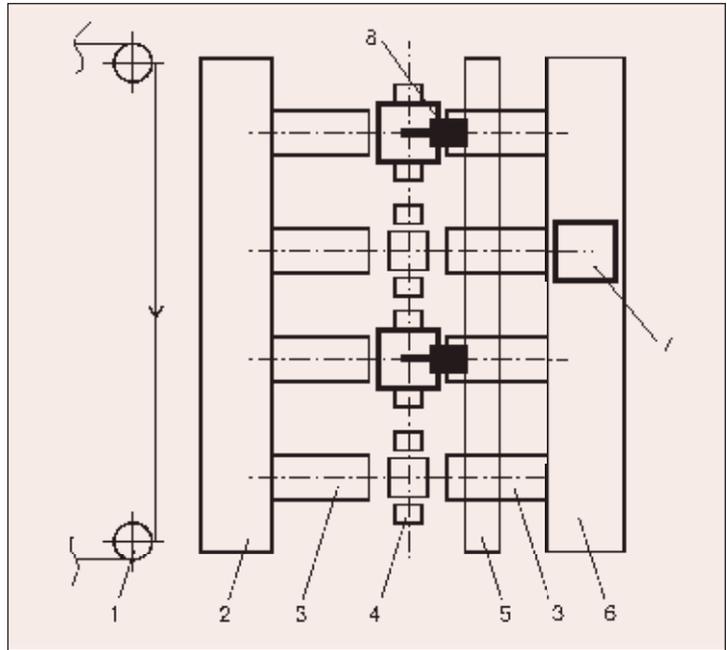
Алгоритм изготовления сварных конструкций в ГПС
